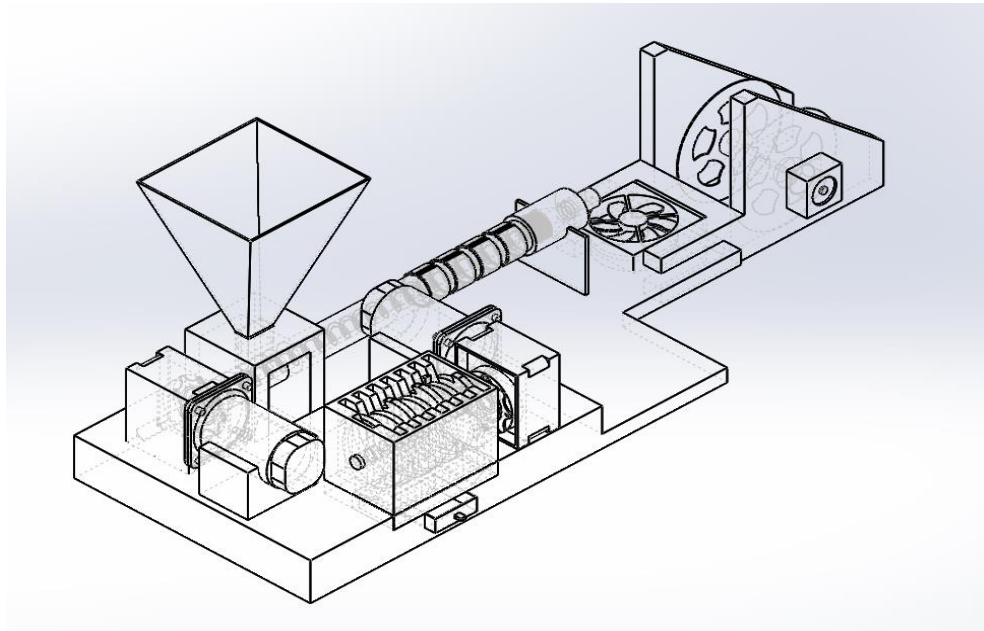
Ensamblaje final de la máquina extrusora vista 1
